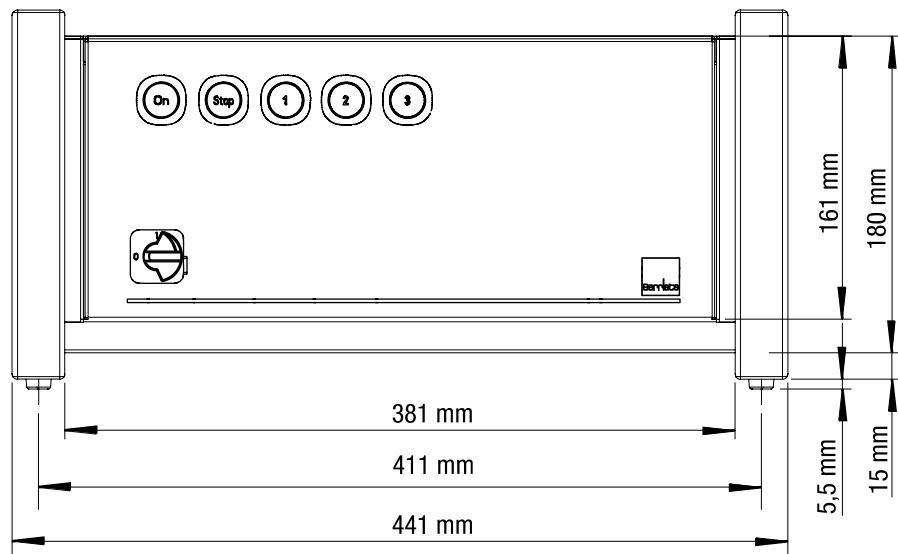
Frontansicht – Steuerung G-FRAME 54 (exemplarisch)
